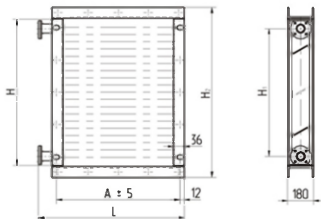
Габаритно присоединительные размеры ВНВ113 ...
